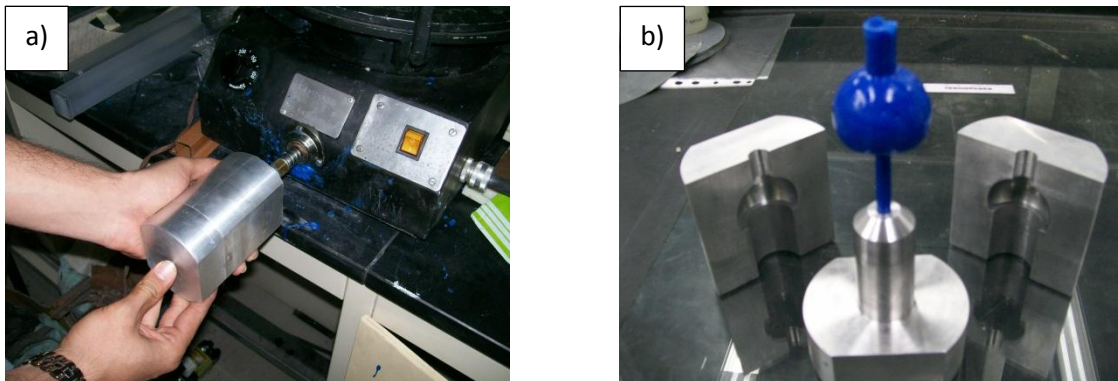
Máquina inyectora de cera, a) molde inyectado y b) patrón de cera en molde.
